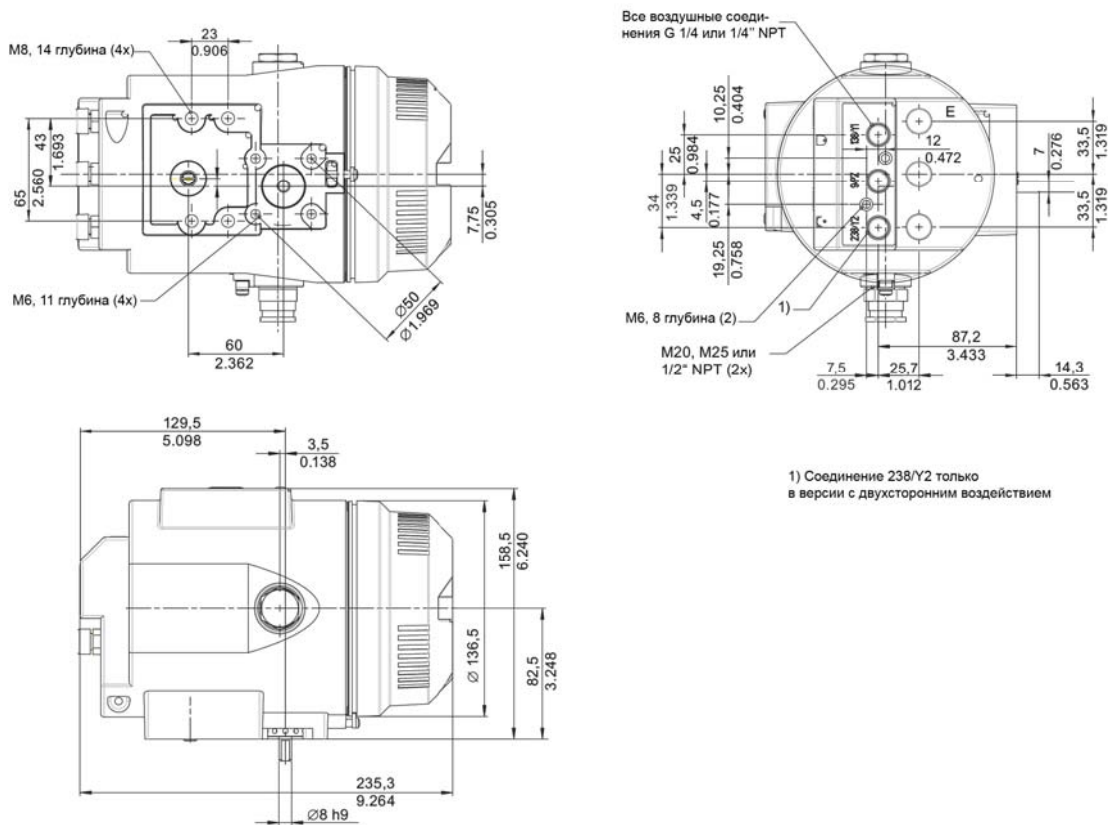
Размеры версии с металлическим корпусом 6DR5xx1
